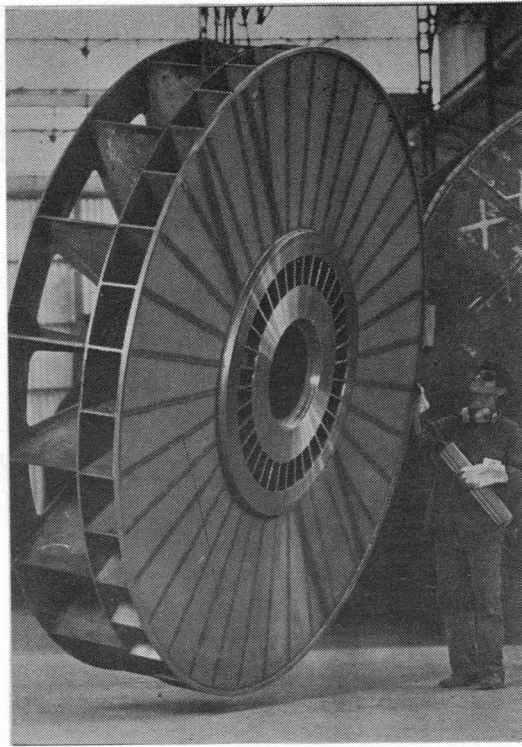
Rotor fabricaado em aço AISI 304L, componente integrante do filtro Corudeck
